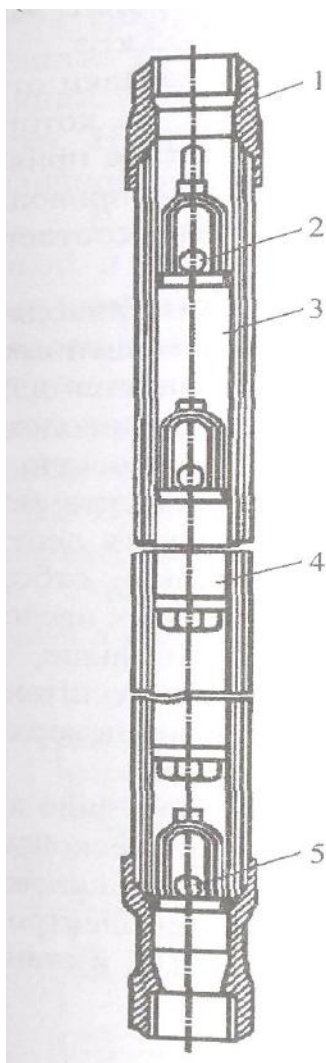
Плунжерный насос 1 - муфта крепления; 2- верхний клапан; 3 - цилиндр; 4-плунжер; 5 - нижний (приемный) клапан
